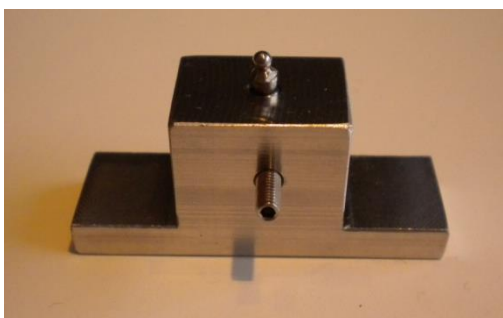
Utillaje de unión inferior con pilar metálico fijado
